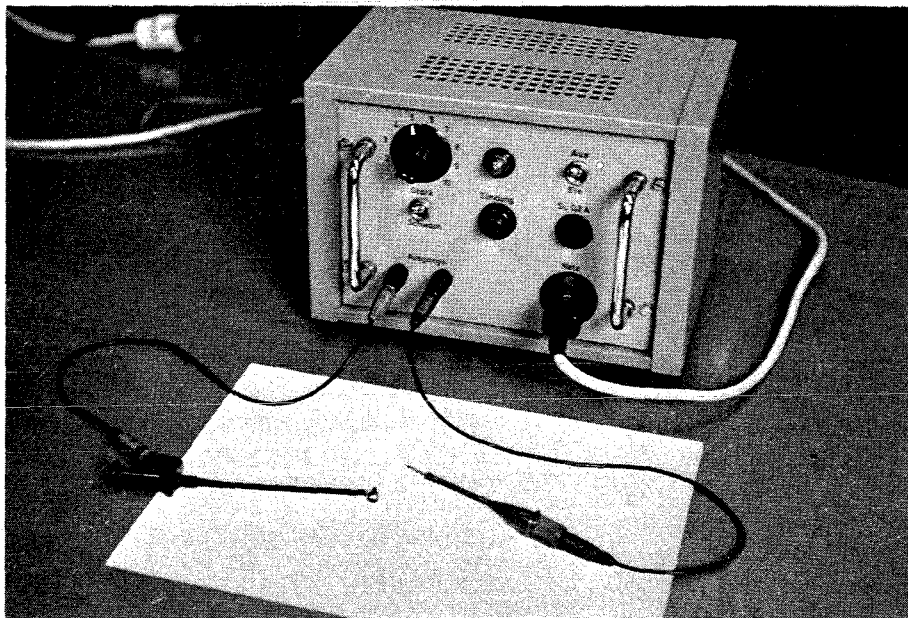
Schweißapparatur für Feinstdrähte mit gesteuerter
